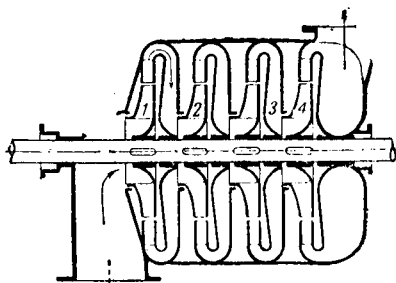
Многоколесный центробежный насос с последовательным соединением колес.
